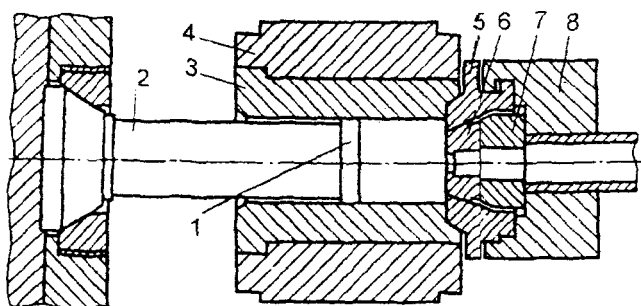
Типовая инструментальная наладка для прессования изделий с прямым истечением
